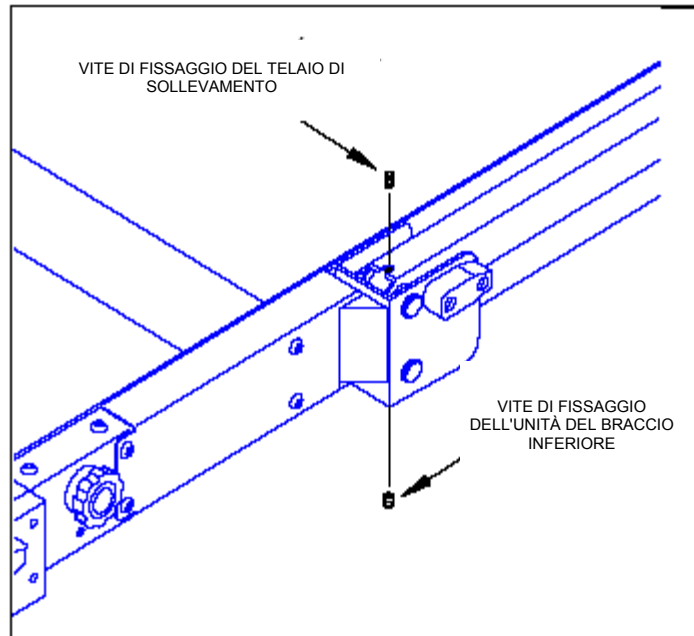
TELAIO DI SOLLEVAMENTO E VITE DI FISSAGGIO DEL BRACCIO INFERIORE
